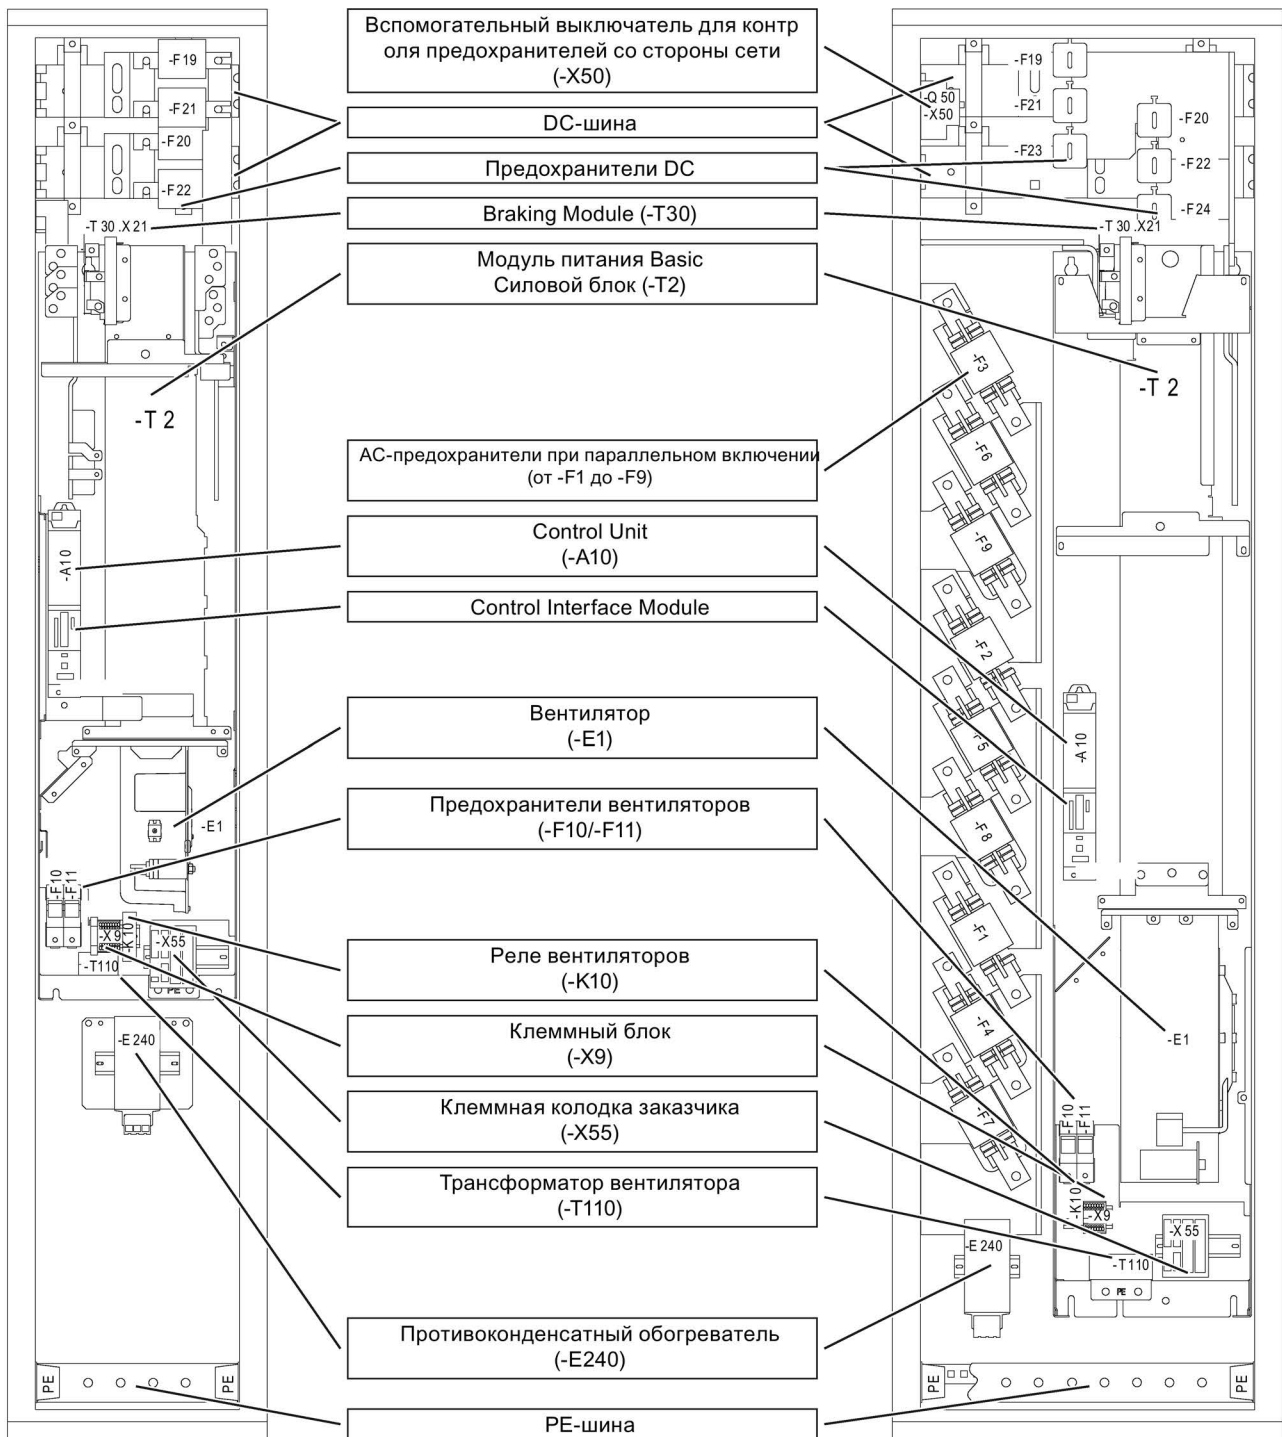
Пример сборки базового модуля питания (типоразмер FB и GD)
